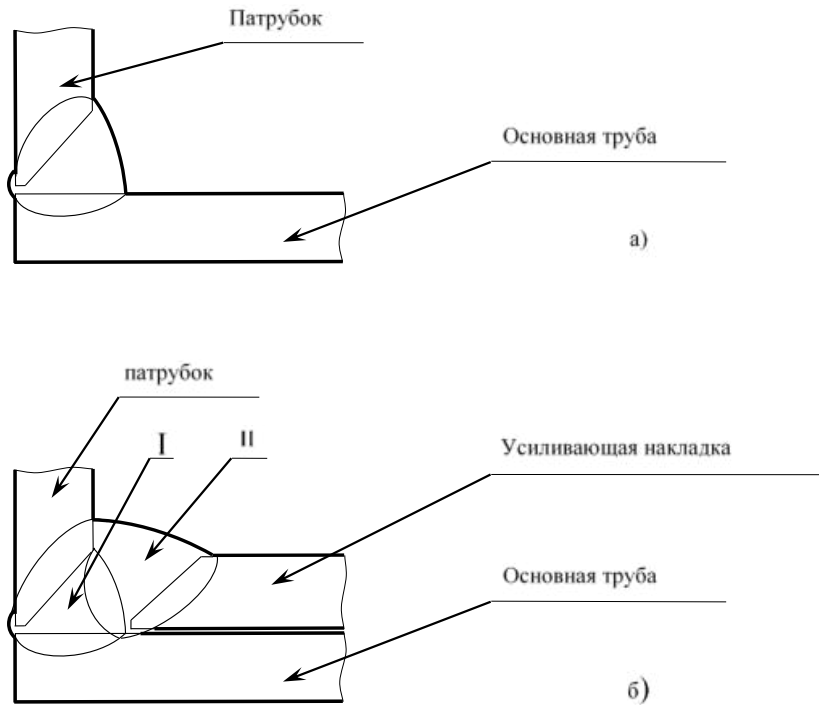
Конструкции угловых сварных соединений тройников, выполненных с усиливающими накладками (б) и без накладок (а)
